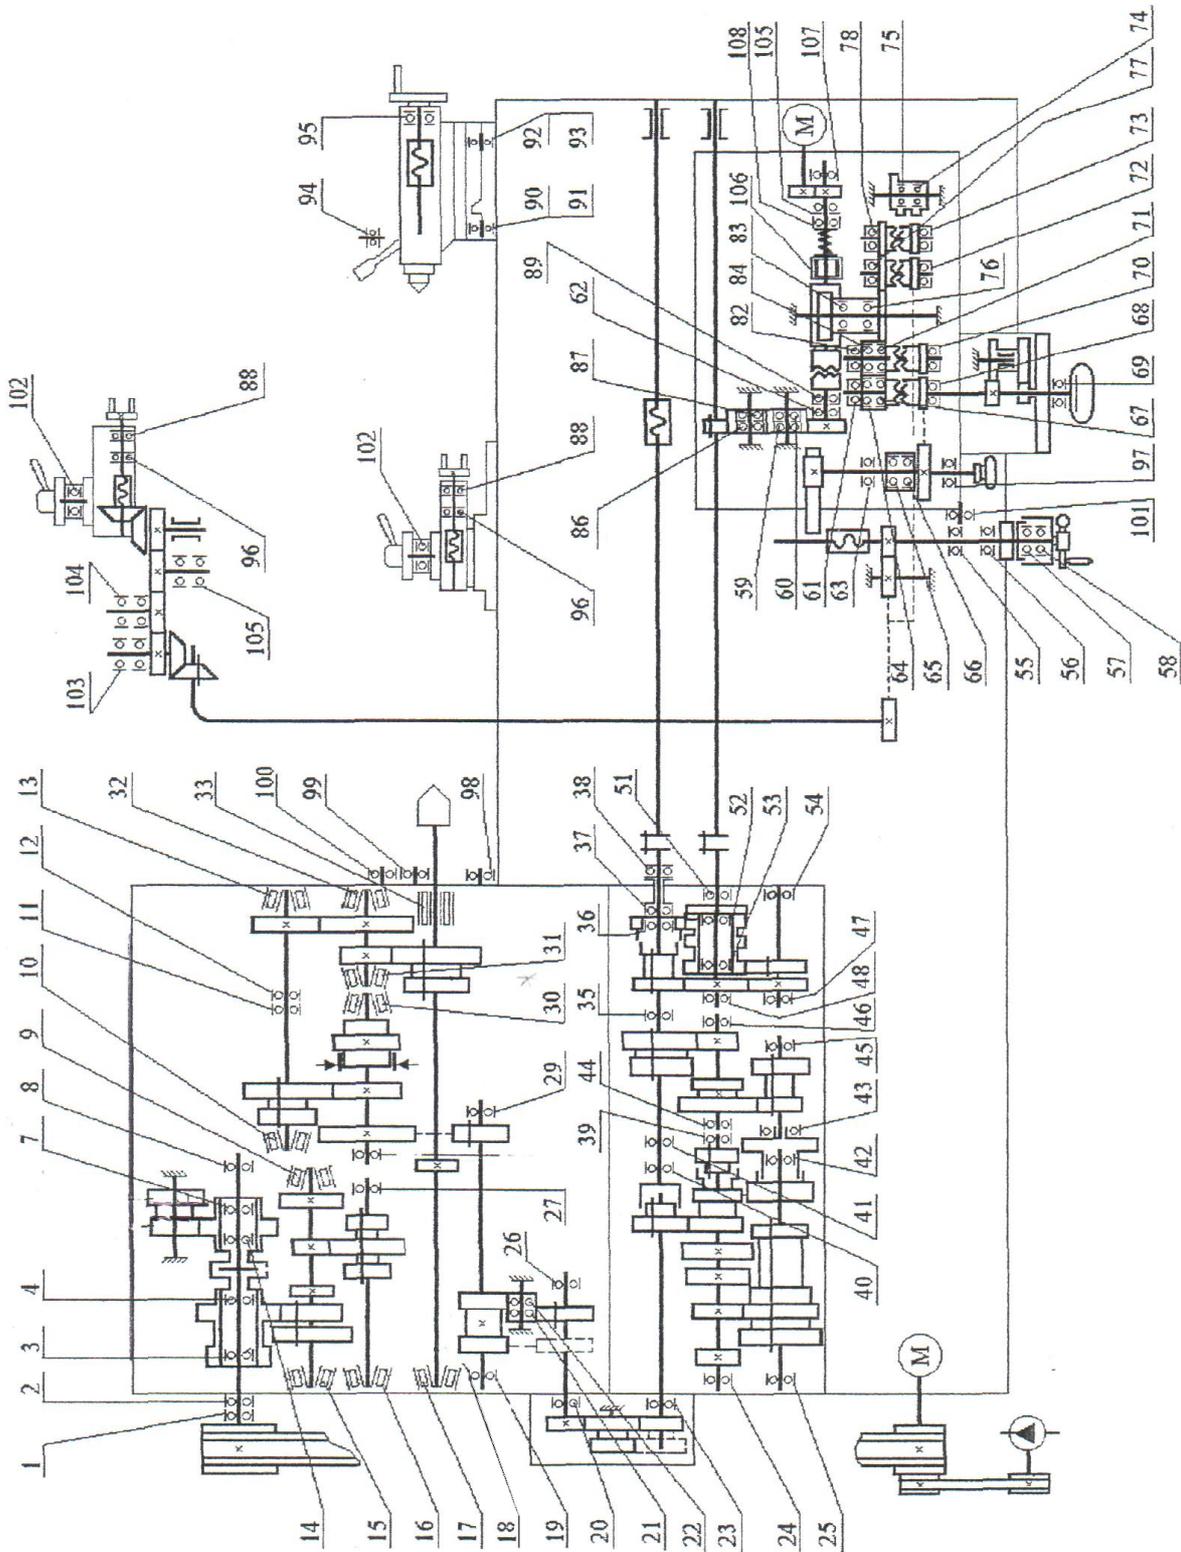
Схема расположения подшипников станка 1B625M (с механизированным суппортом)
